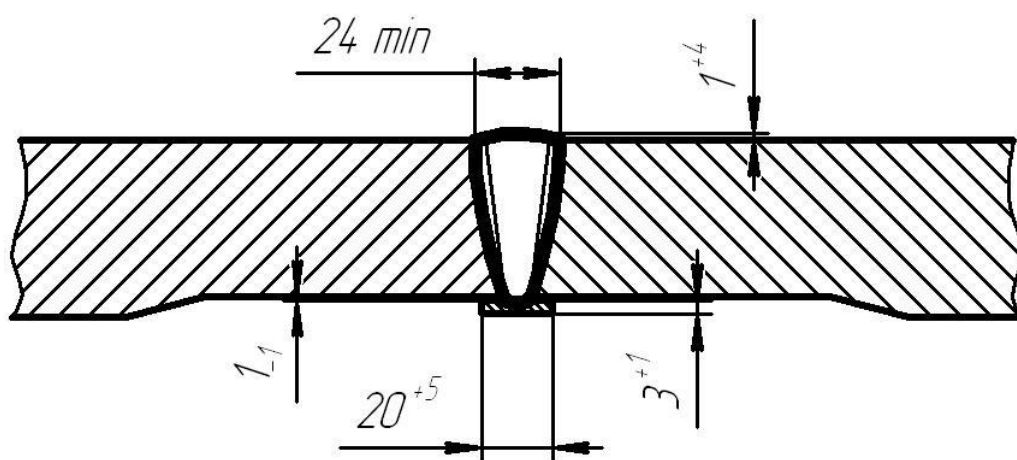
Геометрия сварного шва С4 по ОСТ 108.940.02-82
